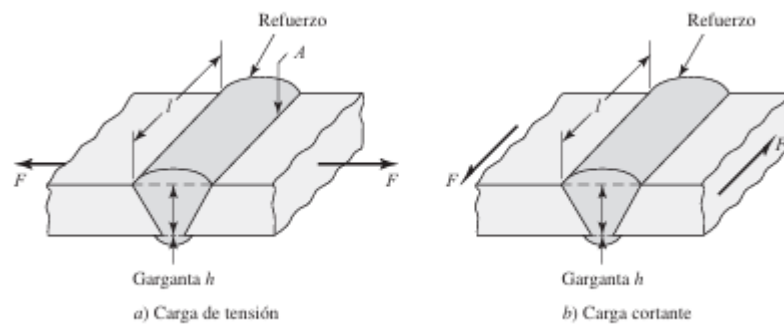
Esfuerzo en una soldadura de ranura tipo V
